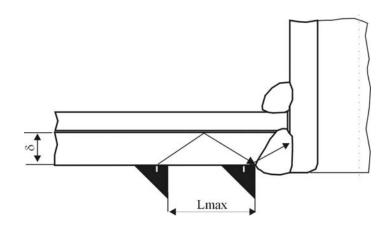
Схема контроля углового шва приварки люка- лаза к стенке PBC
